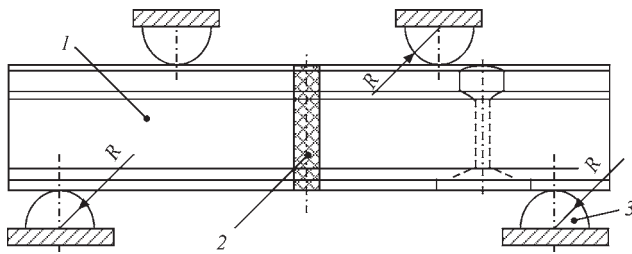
Випробування зварного з'єднання на міцність від утоми: 1 – вид збоку; 2 – зварний шов; 3 – опора
